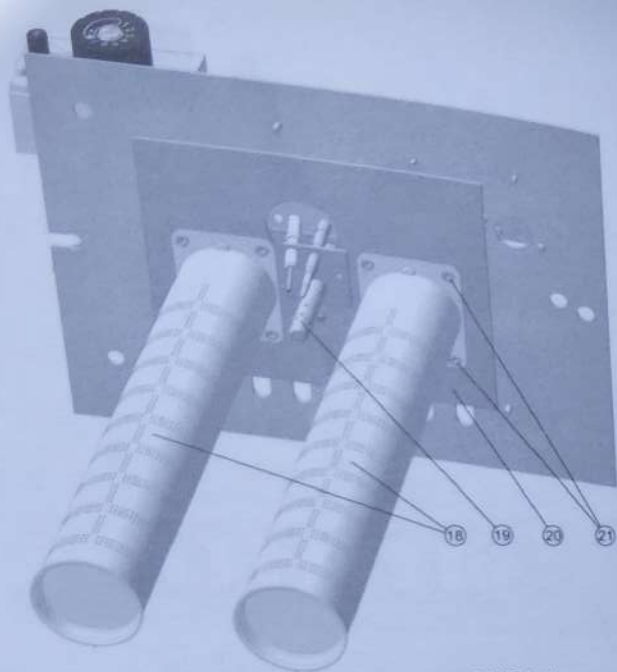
Пристрій газопальниковий ІСКРА (вид ззаду)
